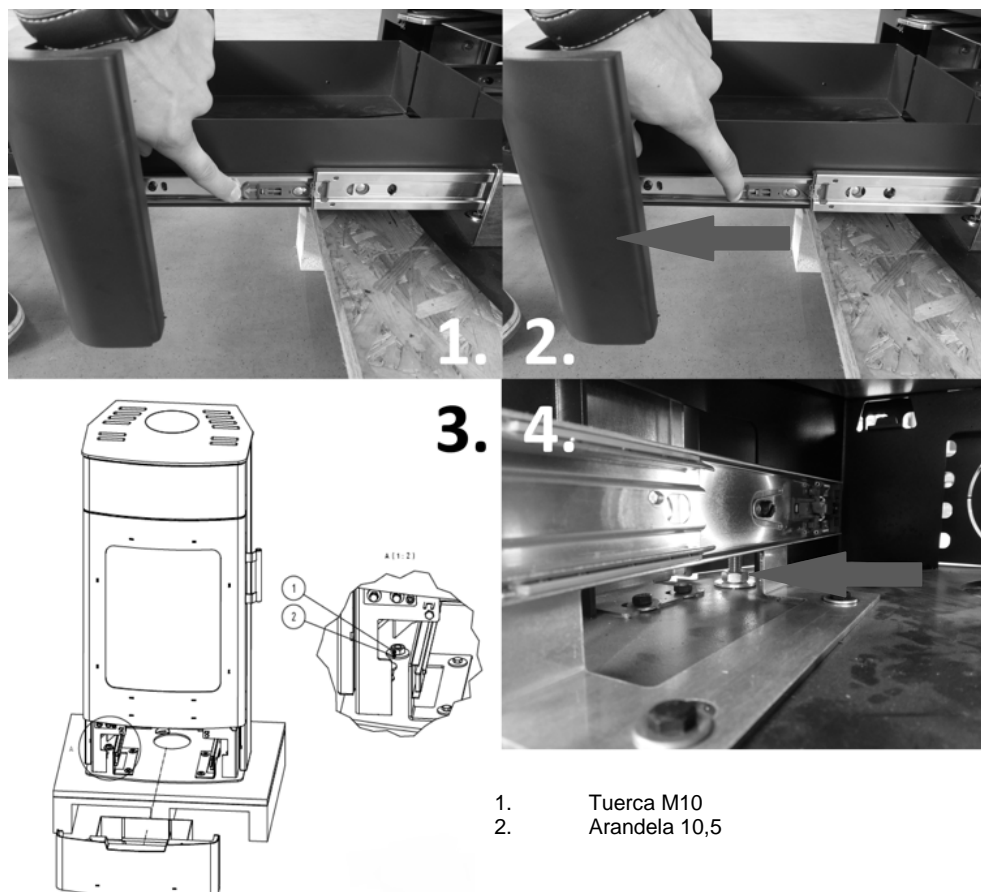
Desmontaje de la estufa de la plataforma de carga
